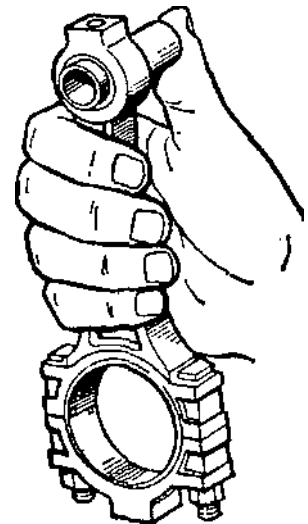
Проверка подбора поршневого пальца к втулке верхней головки шатуна.
